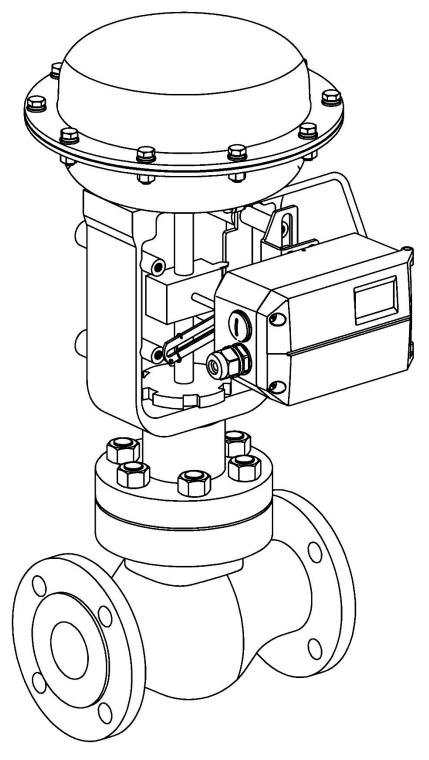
Обычный линейный ход (рычаг обратной связи В)
